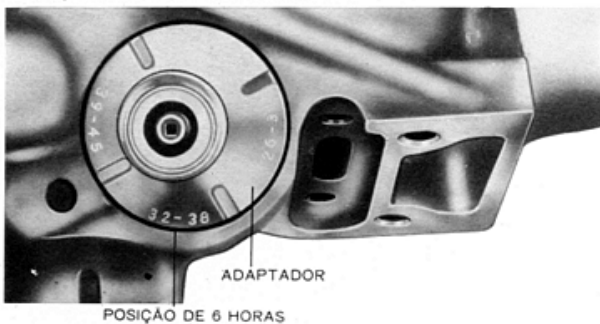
Pinhão do velocímetro e adaptador instalados
